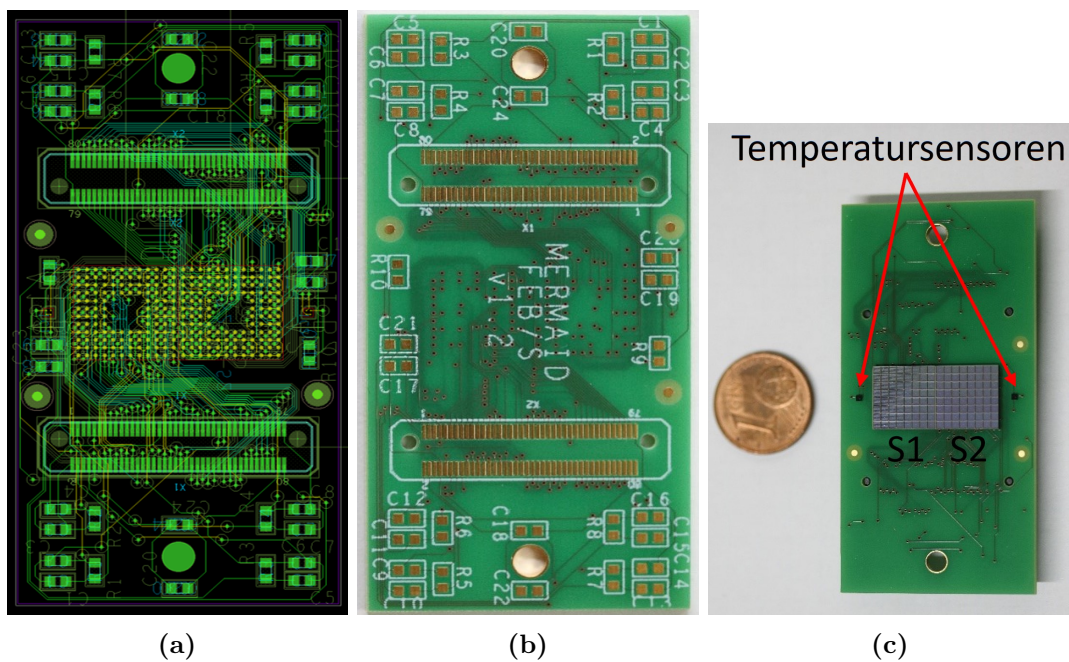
(a) Digitaler Schaltentwurf des PCB als Überlagerung aller Ebenen. (b) Rückseite des PCB mit Kontakten für die jeweiligen Verbindungen zu den ASIC Boards sowie Kontakten für Widerstände zur Filterung der U_{OV} . (c) Vorderseite des PCB mit bereits verlöteten Komponenten. Die beiden SiPMs sind mittig gut zu erkennen. Links und rechts davon sind in Schwarz die Temperatursensoren zu sehen.
